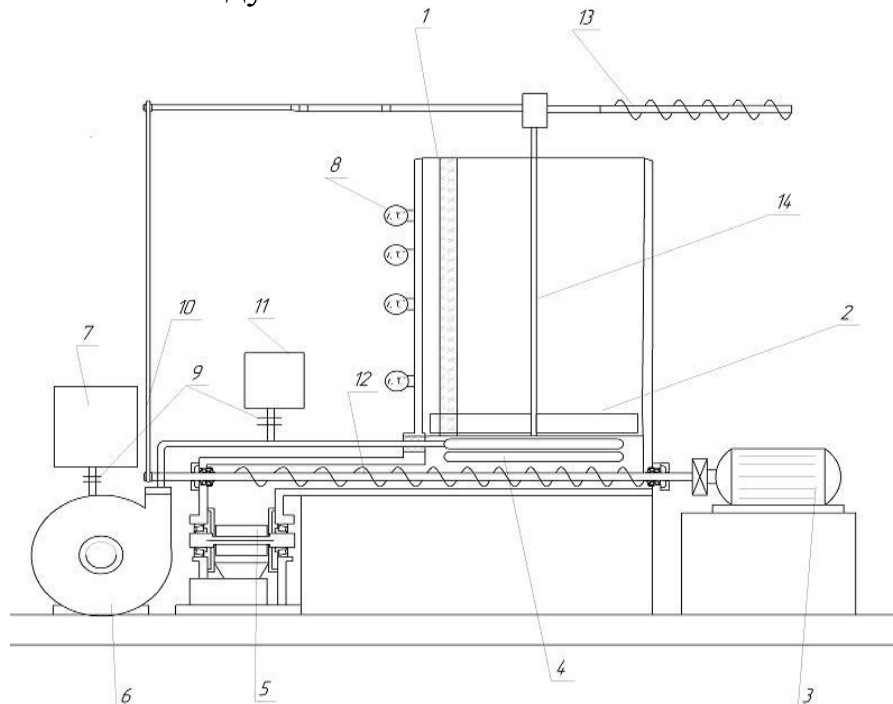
Принципиальная схема установки для вермикомпостирования: 1 – прозрачная вставка; 2 – лопасти мешалки; 3 – привод шнека и конвейера; 4 – ИК-излучатель; 5 – затвор; 6 – компрессор; 7 – теплообменник; 8 – датчик температуры; 9 – электромагнитный клапан; 10 – ременная передача; 11 – увлажнитель; 12 – шнек выгрузки готового продукта; 13 – шнек загрузки субстрата; 14 – вал.
